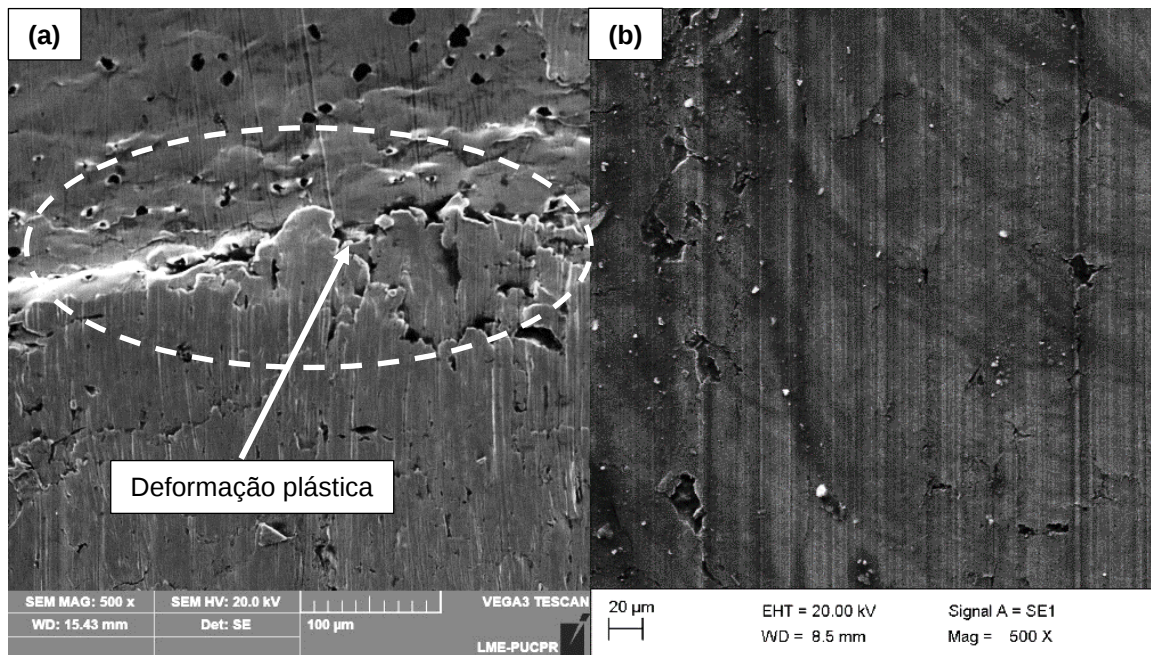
Imagens de MEV (a) matriz posição S (b) chapa DP980
